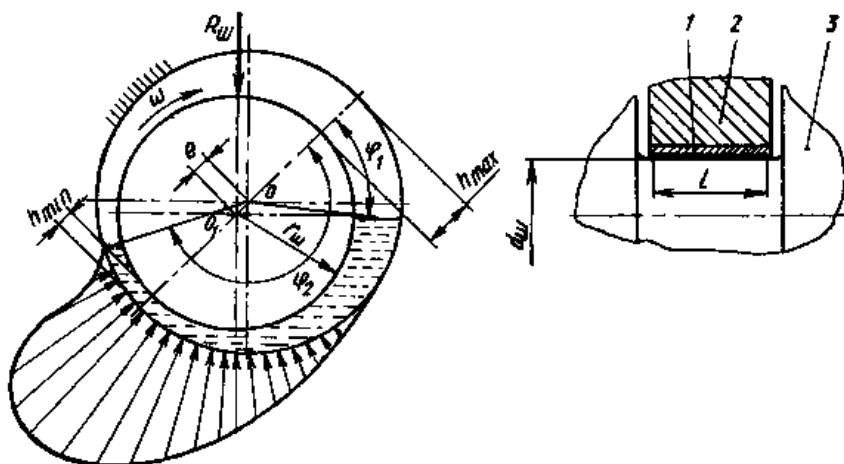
Положение вала в подшипнике и конструктивная схема подшипника:
